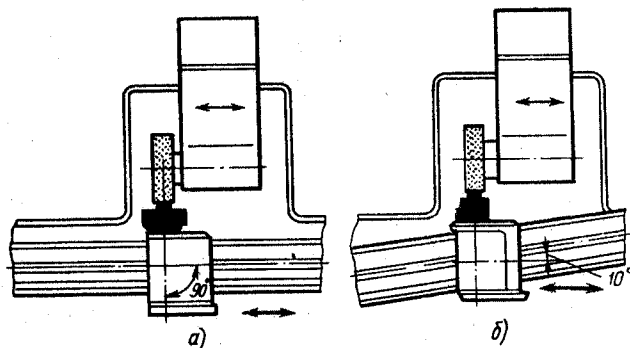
Схема наладки станка для шлифования плоских поверхностей фланцев:
